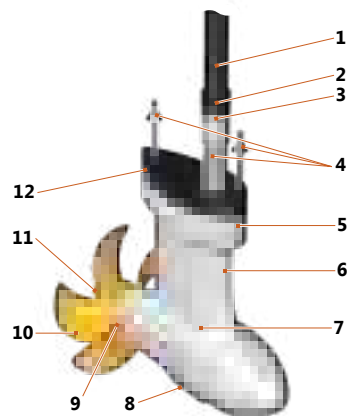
Vista general de las piezas de accionamiento y los componentes
